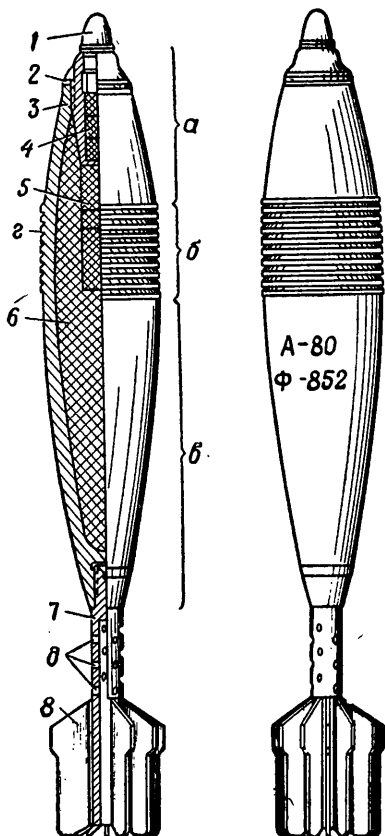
Общий вид и вертикальный разрез 160-мм фугасной мины:
